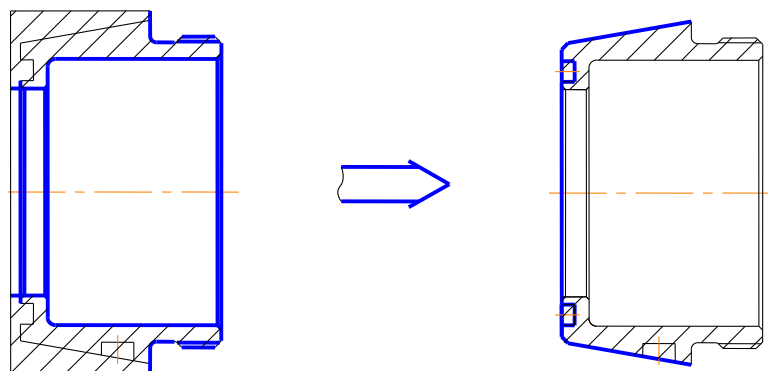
Переустановка заготовки при обробці з іншої сторони на другій шпиндельній бабаці
